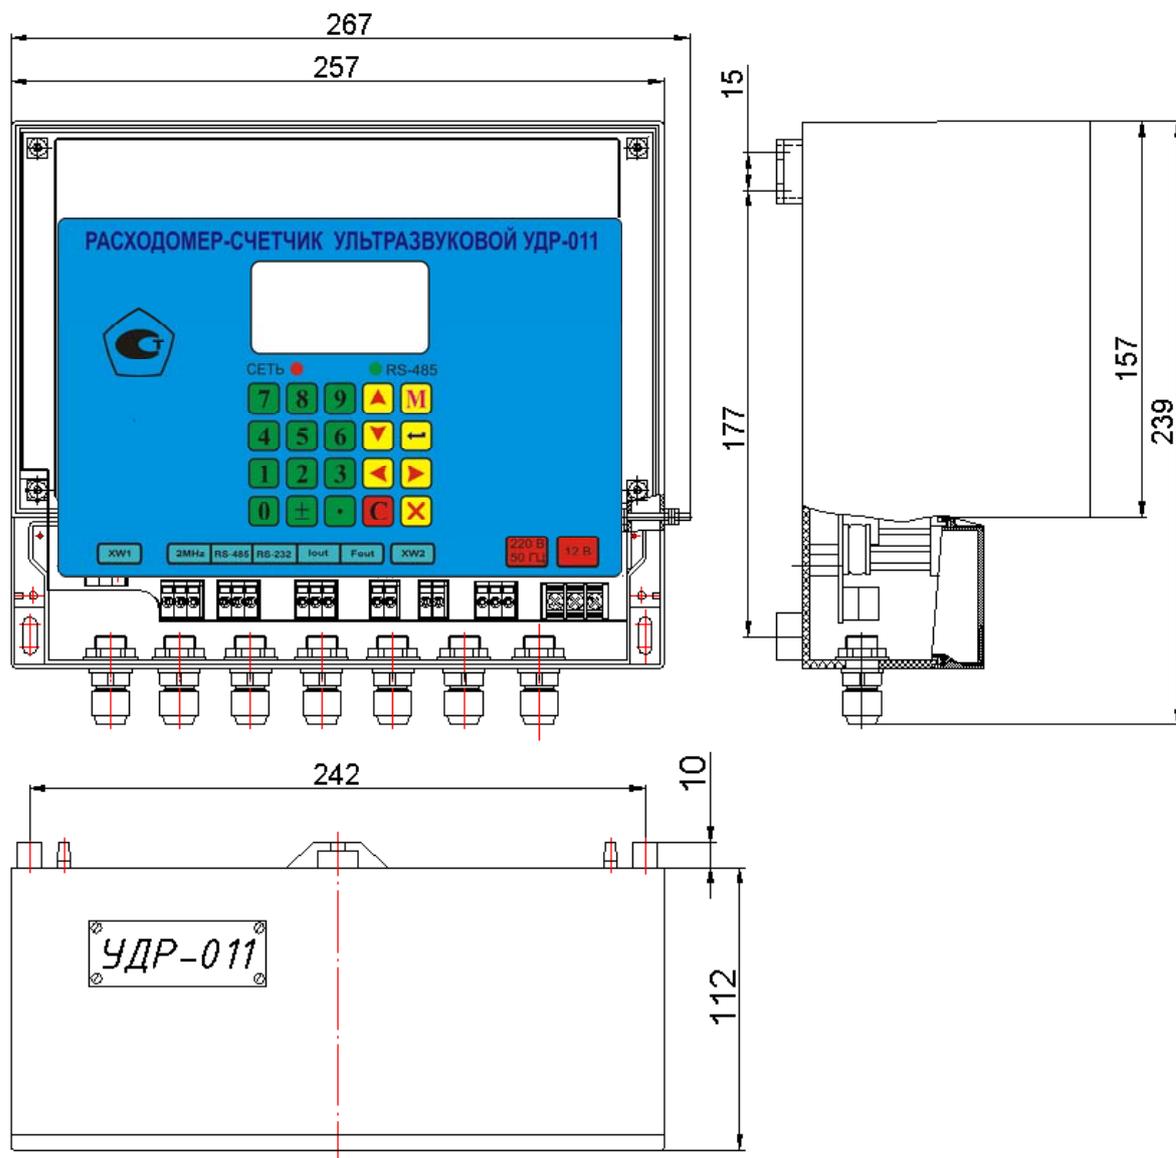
Внешний вид, габаритные и установочные размеры БЭ УДР-011
